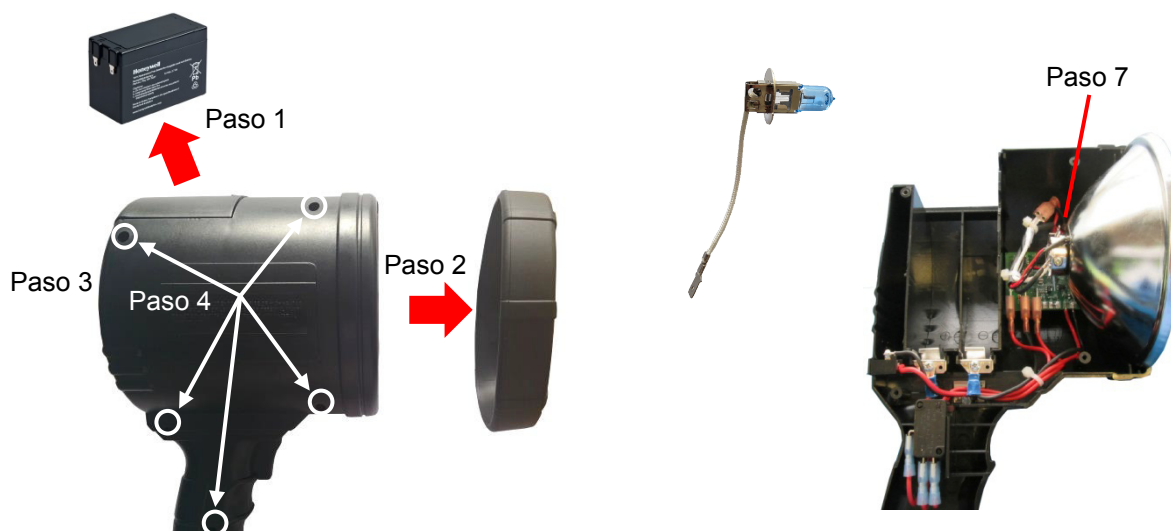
Vista desarrollada de la sustitución de la bombilla FSL100-TL
